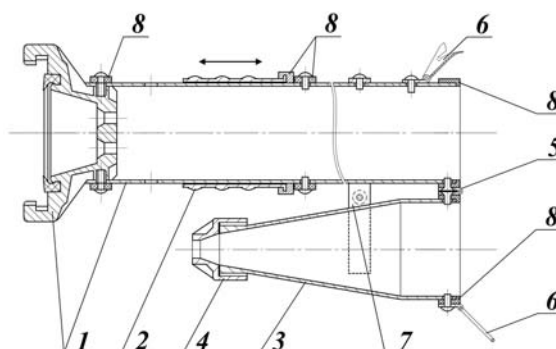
Ствол комбінований водопінний СКВП (положення для подачі повітряно-механічної піни низької кратності): 1 – корпус (ствол повітряно-пінний типу СПП); 2 – трубчаста заглушка; 3 – конусоподібна частина; 4 – змінна насадка; 5 – рухомий шарнір; 6 – кріплення для з'єднання корпусу та конусоподібної частини; 7 – підтримуючий хомут; 8 – ущільнювачі.
